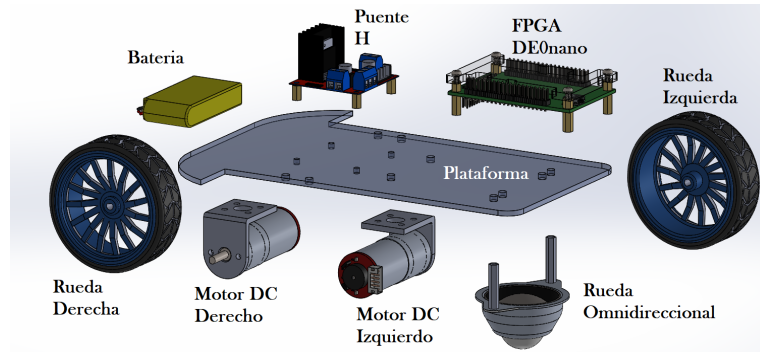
Piezas diseñadas en CAD para el ensamble del robot líder.
